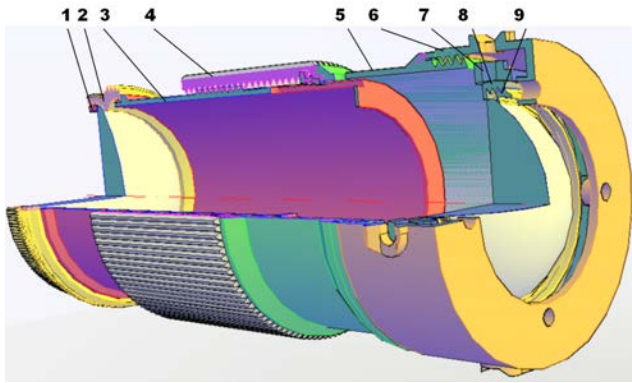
Оптико-механічний пристрій з вузлом юстирування однієї з лінз: 1 – кільце різьбове; 2 – оправа першої лінзи; 3 – тубус внутрішній; 4 – тубус зовнішній; 5 – тубус проміжний; 6 – кільце зовнішнє; 7 – втулка сферична; 8 – корпус сферичний; 9 – оправа другої лінзи
